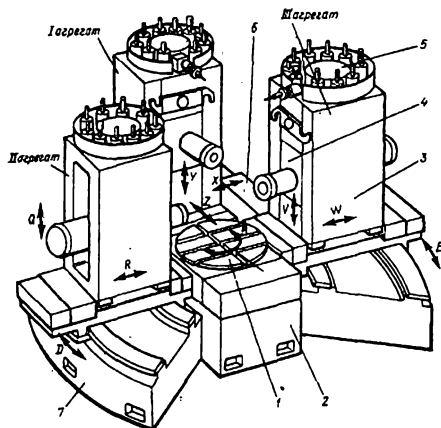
Компонівка агрегатного верстата з ЧПУ
